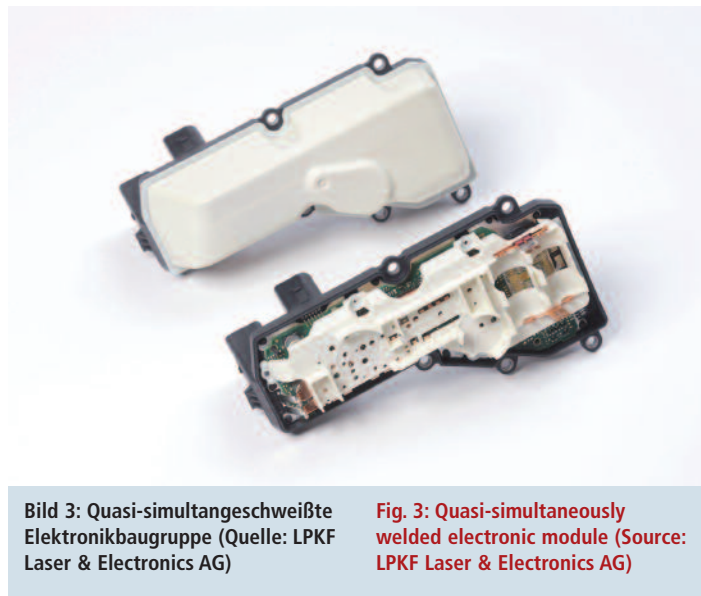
Quasi-simultangeschweißte Elektronikbaugruppe (Quelle: LPKF Laser & Electronics AG)
